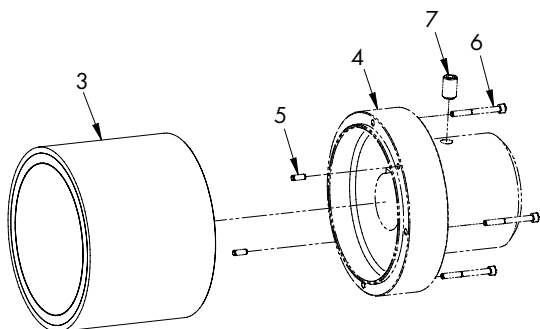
Montaggio del rotore esterno sul lato motore (opzionale) (A3)
